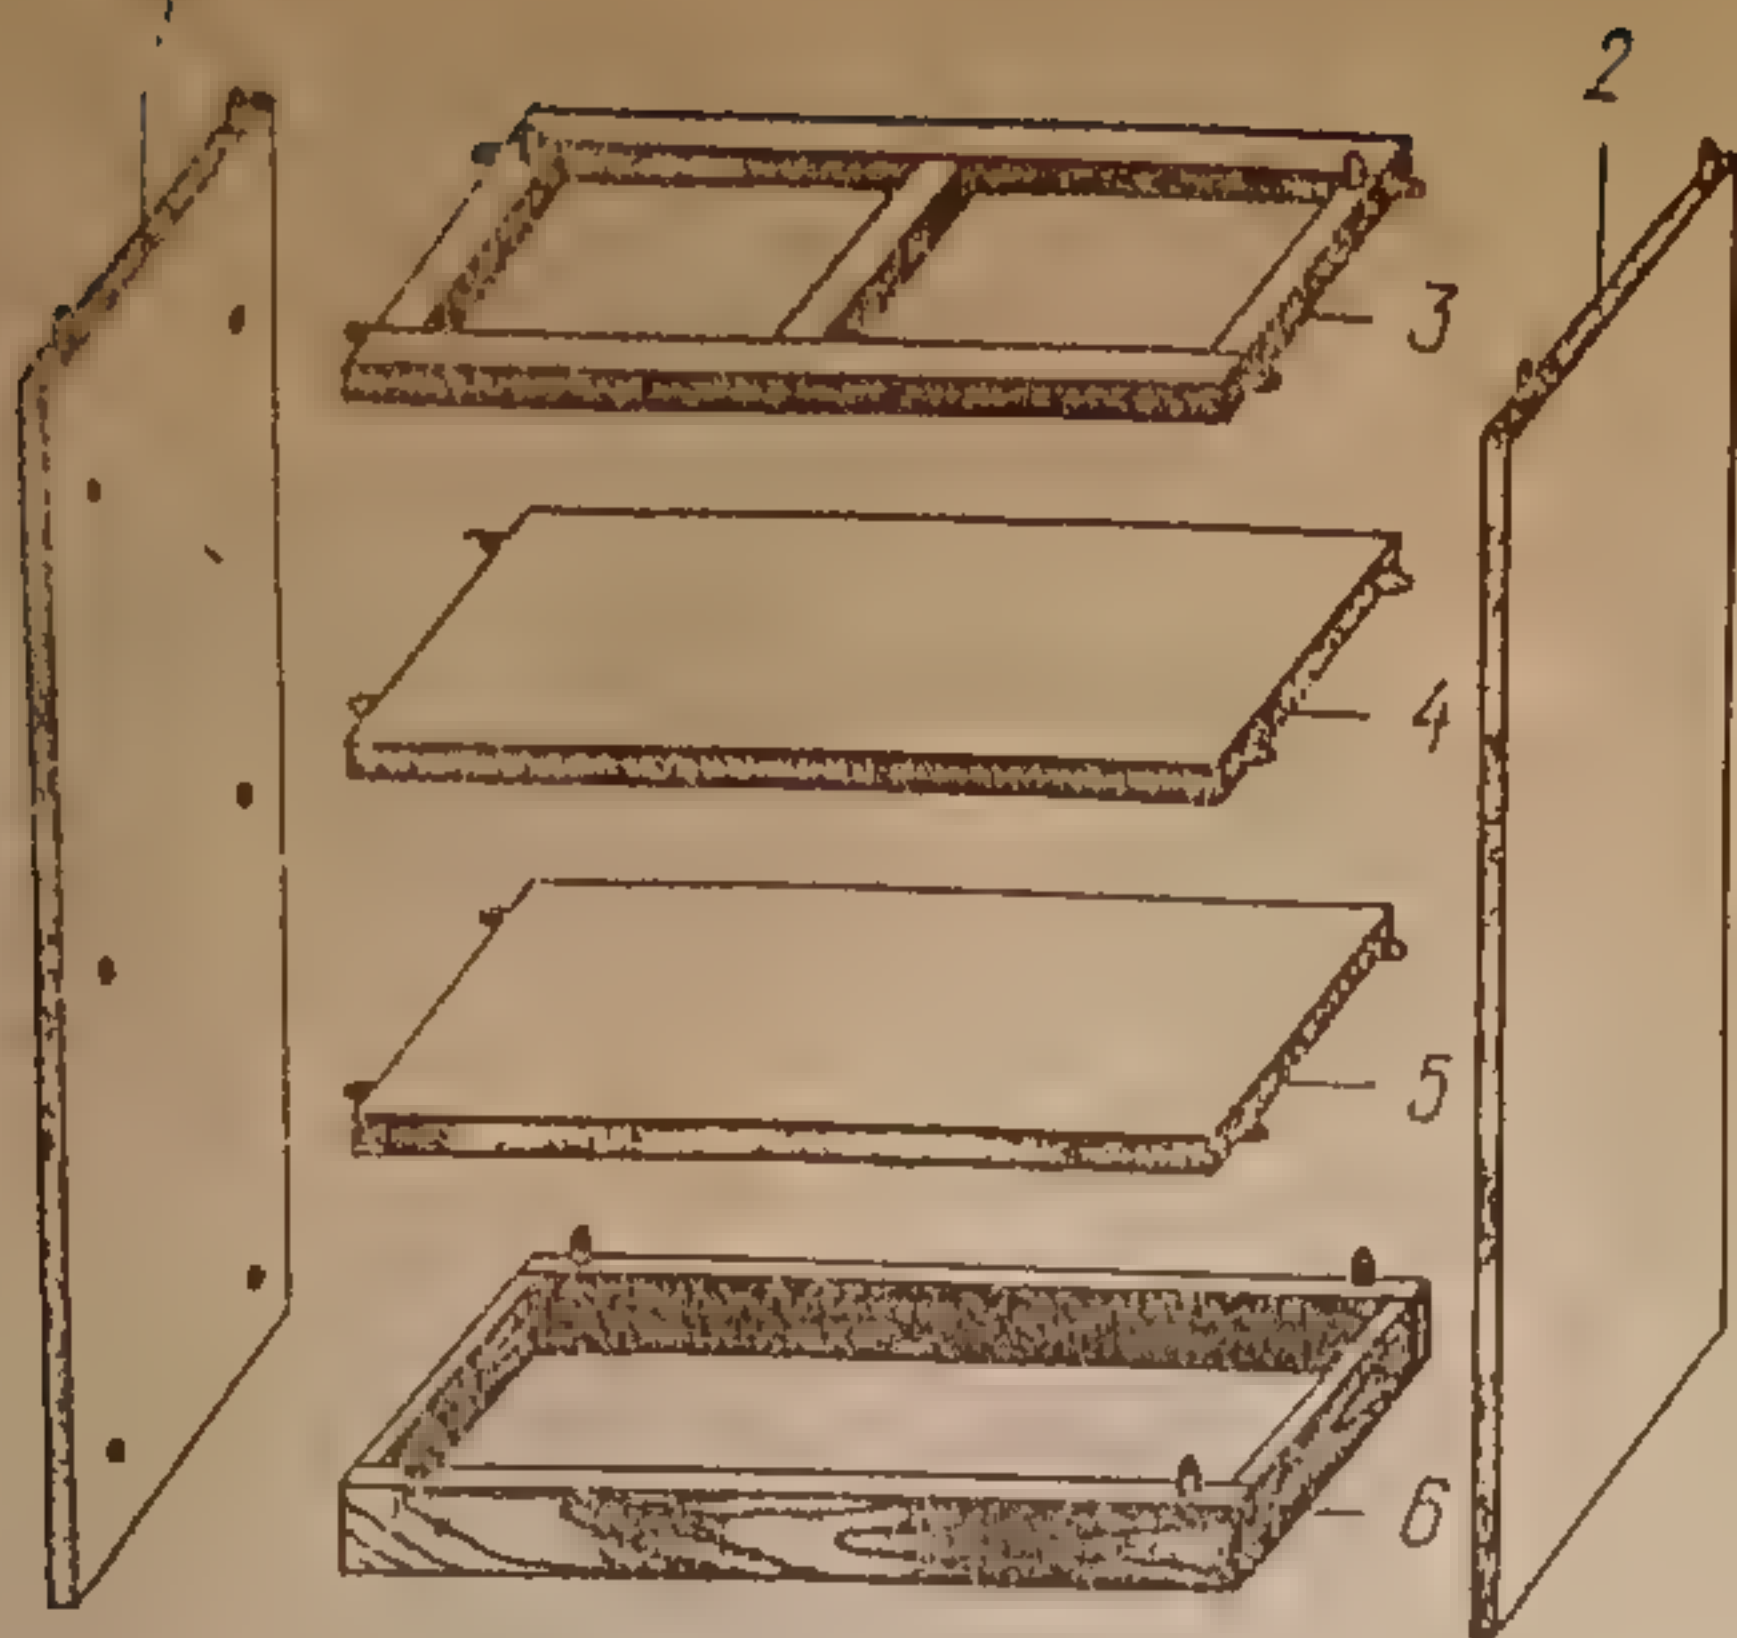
Детали разделочного шкафа со вставными шпильками: 1 и 2 — боковые стенки; 3 — подъящичная рамка; 4 — полка; 5 — днище; 6 — цоколь
